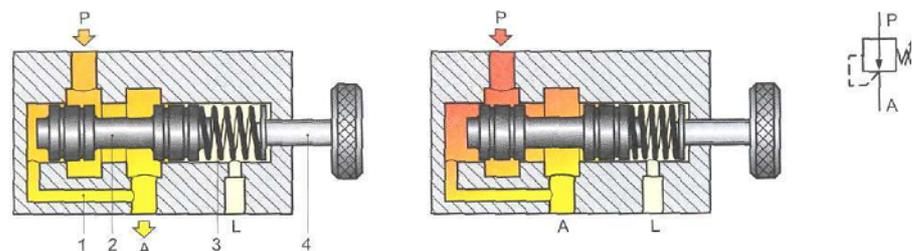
Двухлинейный редуцирующий клапан прямого
